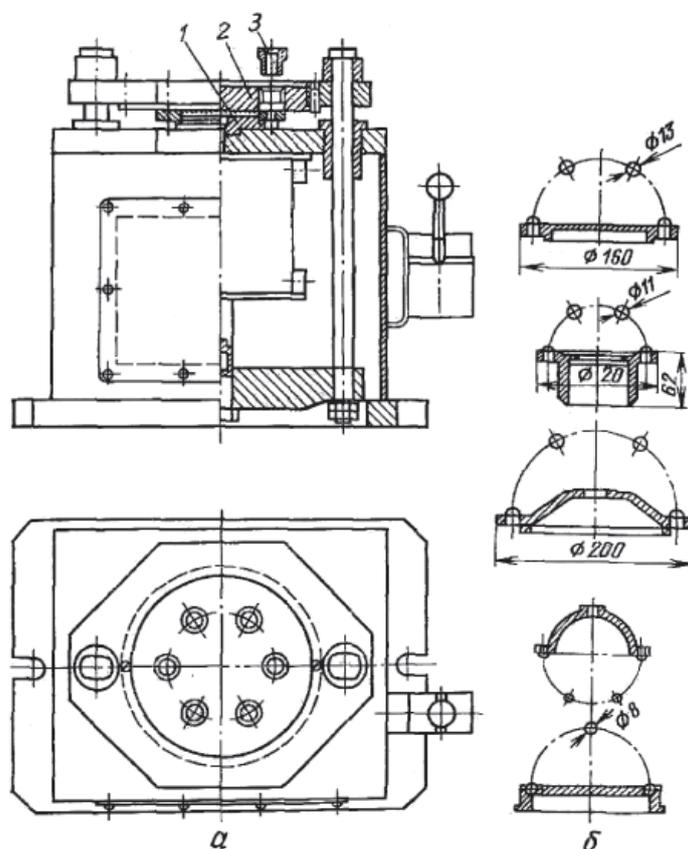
Портальный скальчатый кондуктор со сменными наладками
